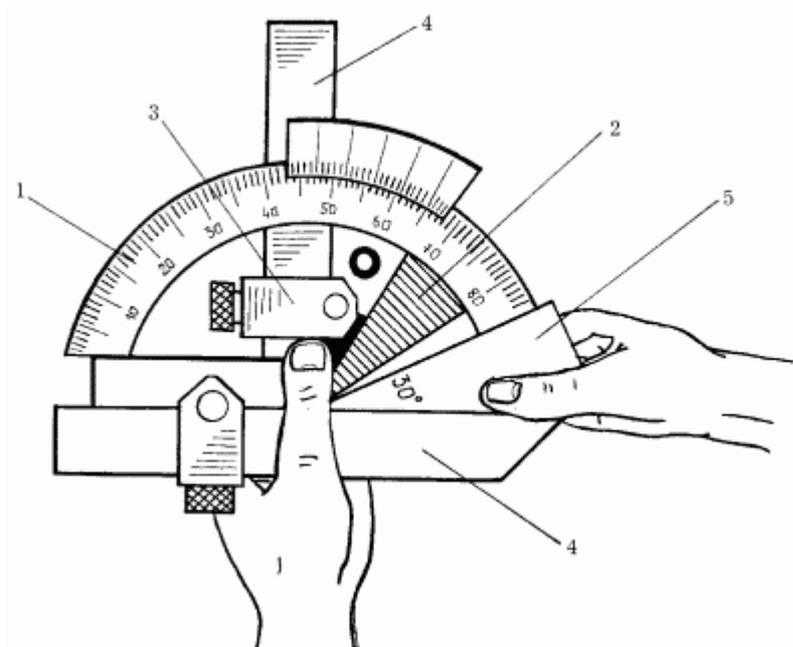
Угломер: 1 – полудиск со шкалой; 2 – подвижный сектор с нониусом; 3 – стопорный винт; 4 – линейка; 5 – измеряемая деталь.
